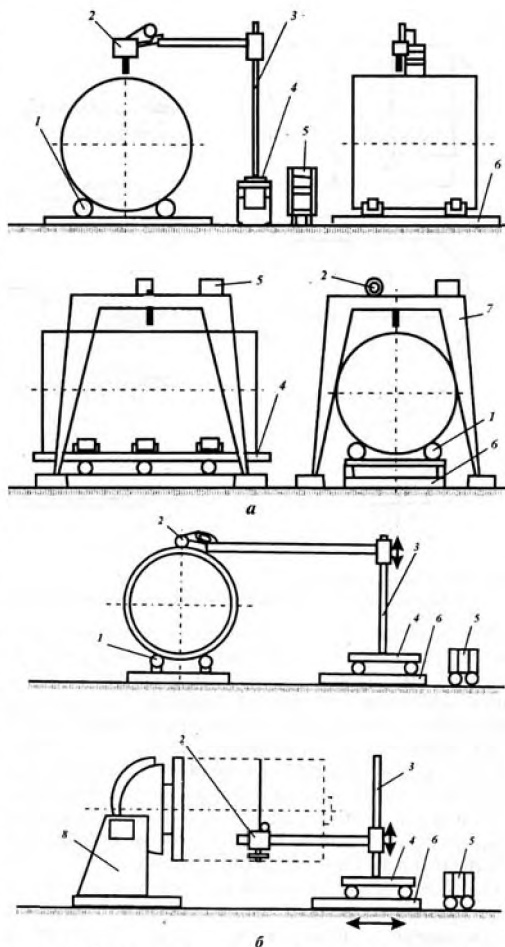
Компонентные схемы стенов для сварки прямолинейных и кольцевых цилиндрических и конических обечайек: 1 — манипулятор роликовый; 2 — сварочный автомат; 3 — колонна с консолью; 4 — тележка; 5 — источник питания; 6 — направляющие; 7 — портал; 8 — манипулятор
